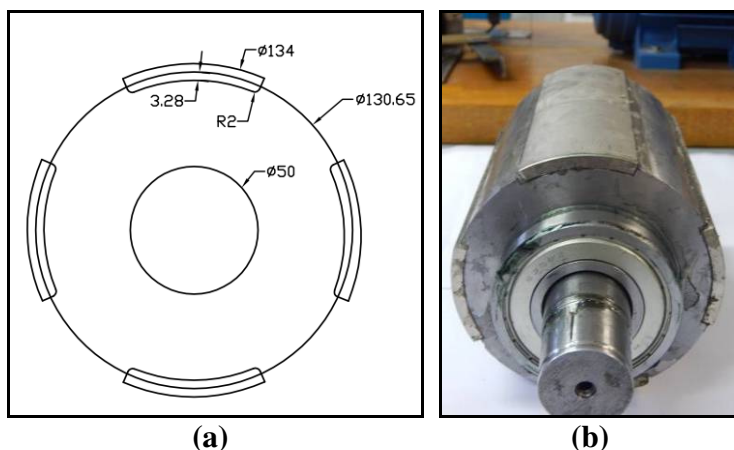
Rotor de polos lisos – (a) Desenho esquemático – (b) rotor montado [30]
